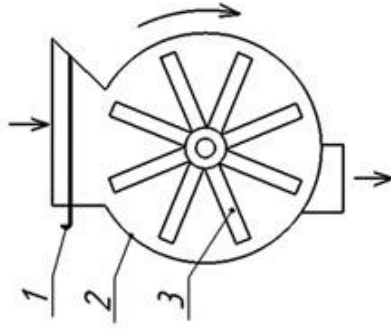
Барабанний Дозатор: 1 - заслінка; 2 - корпус; 3 - лопатевої барабан
